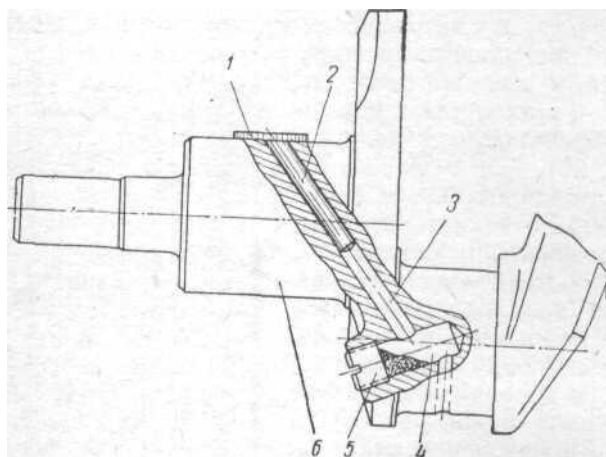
Установка приспособления для выталкивания вкладыша коренного подшипника из постели блока цилиндров:
